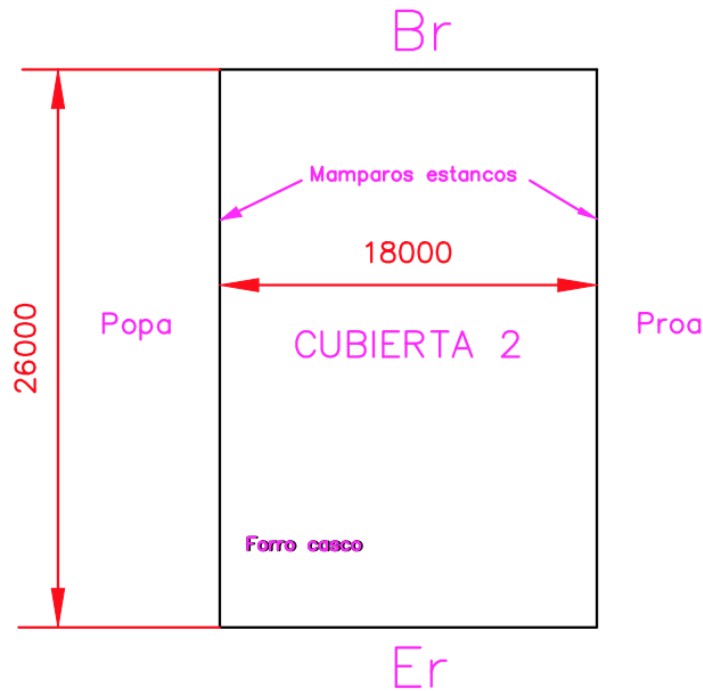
Vista planta Cubierta 2. Elaboración propia AutoCad.
